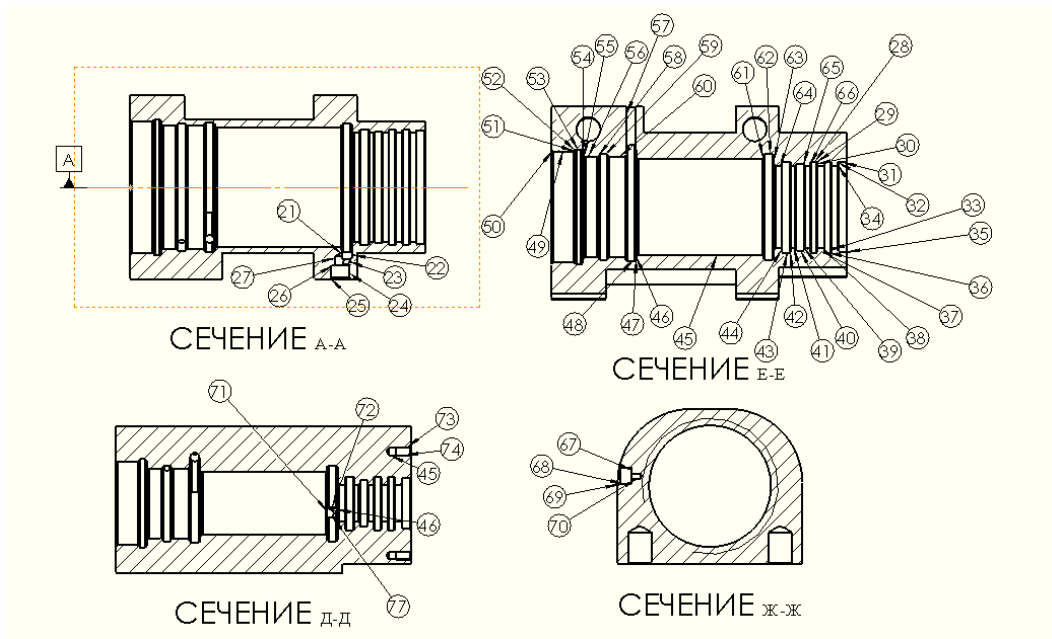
(В) — Ескіз корпусу з нумерацією поверхонь
